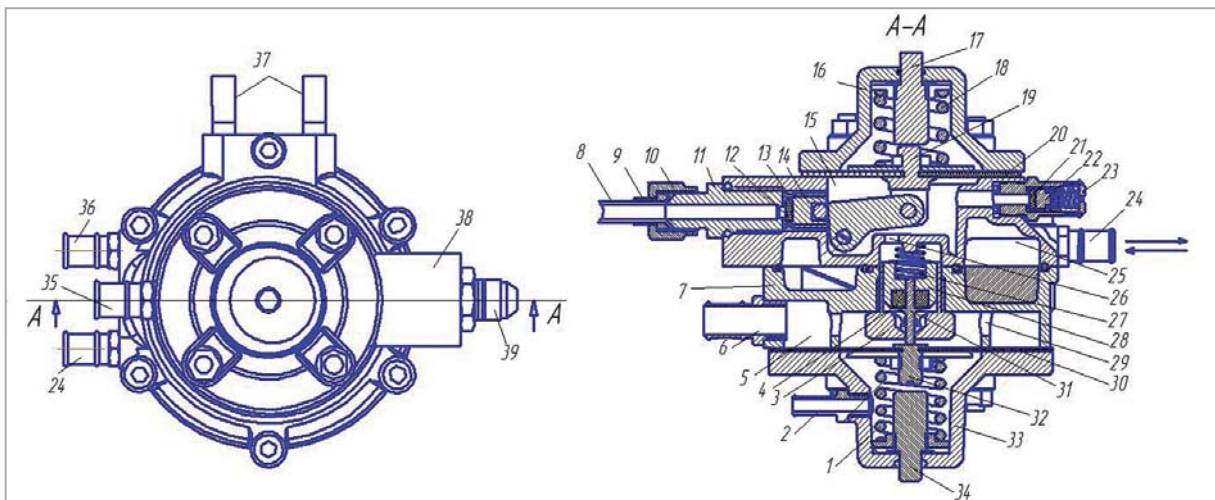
Двухступенчатый газовый редуктор высокого давления:
